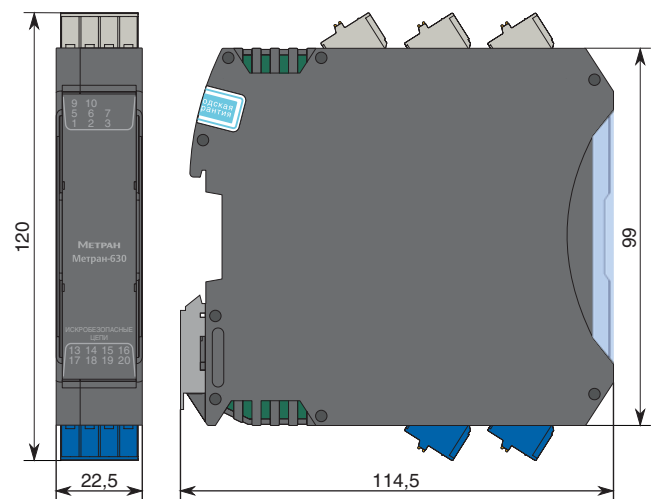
Габаритные размеры барьера в корпусе шириной 22,5 мм с разъемами с пружинными клеммниками и тестовыми гнездами
